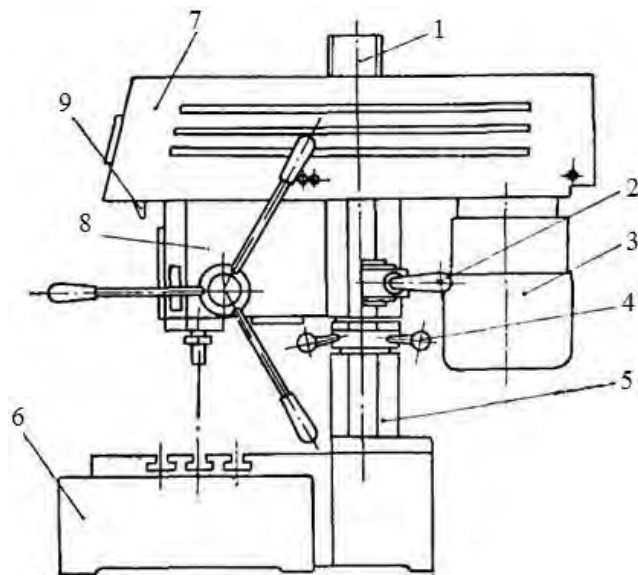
Основные части станка модели 2М112-BC327:
